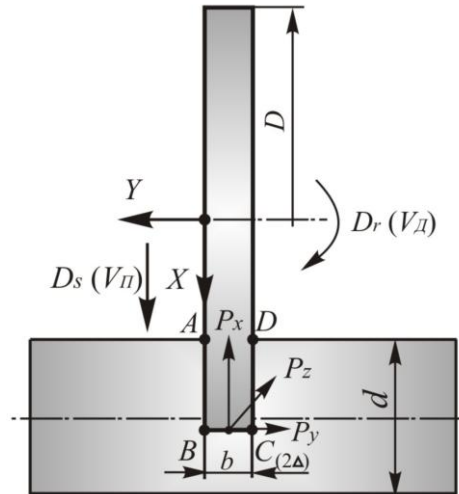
Схема зони контакту дискової пили тертя і заготовки при ЕФР
